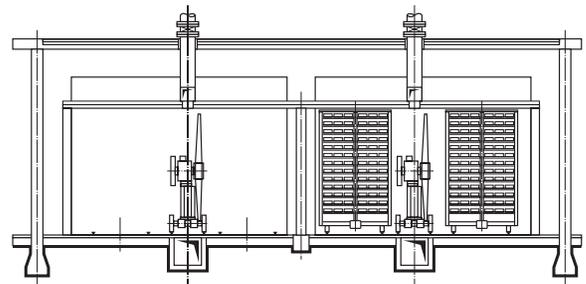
Реконструкция сушильной камеры с использованием осевых вентиляторов и заменой сушильной оснастки (реек) на каркасные вагонетки
